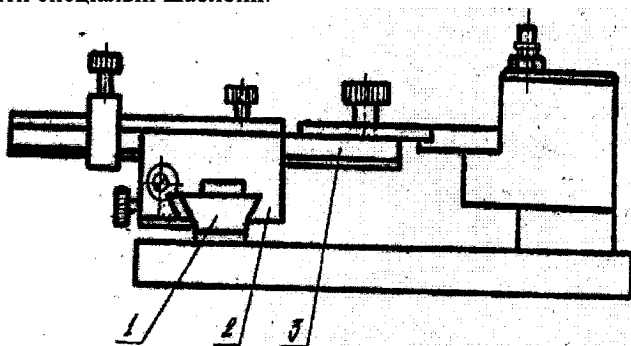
Налагодження інструмента поза верстатом за допомогою пристосування
